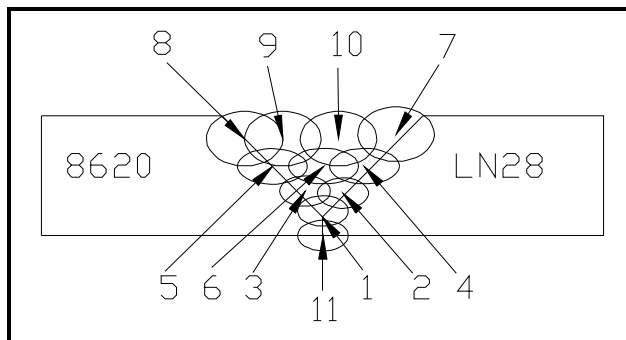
Seqüência de passes utilizada no processo de soldagem dos corpos de prova.
